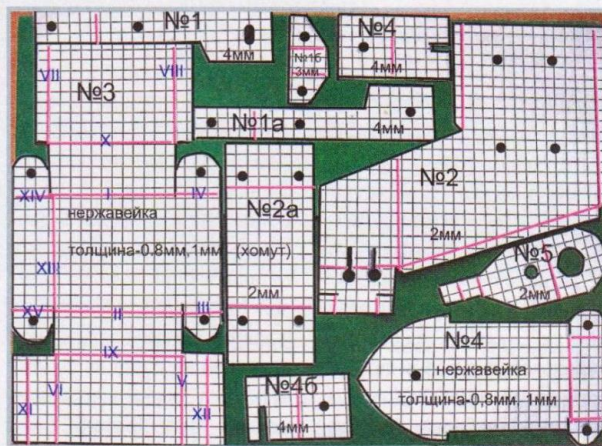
Комплект заготовок, выкраиваемых из листового металла. Толщина листа обозначена на каждой заготовке, места изгибов отмечены красными линиями. Для детали №3 указана рекомендуемая последовательность изгибов. Шаг координатной сетки — 5 мм.
